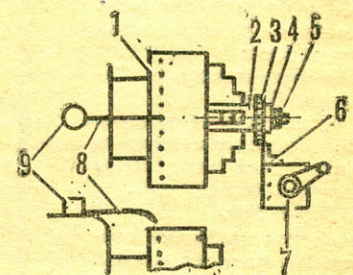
Патрон токарного станка — делительная головка: 1 — патрон, 2 — оправка, 3 — подлежащая разметке деталь, 4 — шайба, 5 — гайка, 6 — резец-чертилка, 7 — резцедержатель, 8 — игла-указатель, 9 — грузик.
